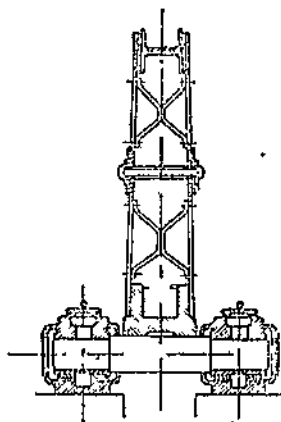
Направляющий шкив для круглого каната со сдвигами из швеллеров.
